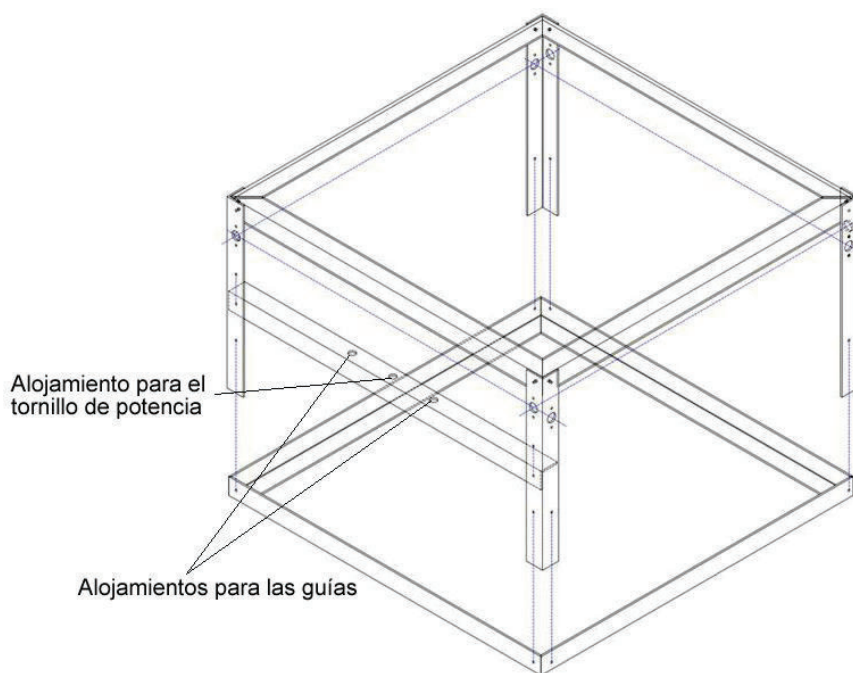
Esquema del procedimiento de montaje de los perfiles horizontales inferiores de la estructura.
